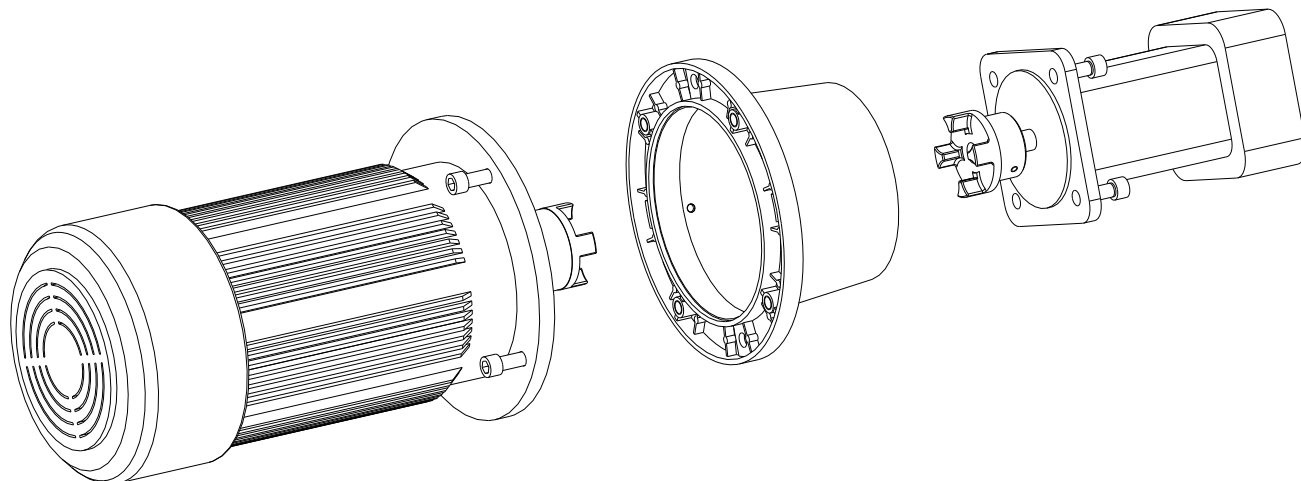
Montaggio motore elettrico e/o pompa con lanterna
